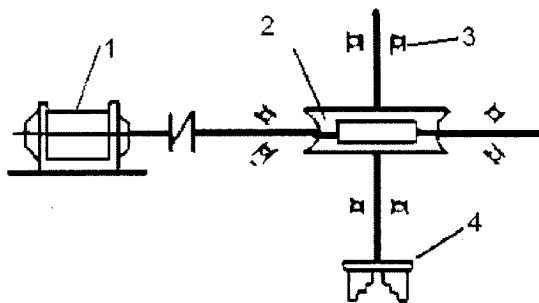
Кінематична схема механізму ВМС-12 для прорізання й згинання сталевих труб: 1 — електродвигун; 2 — черв'ячний редуктор; 3 — люнет; 4 — трикулачковий патрон
